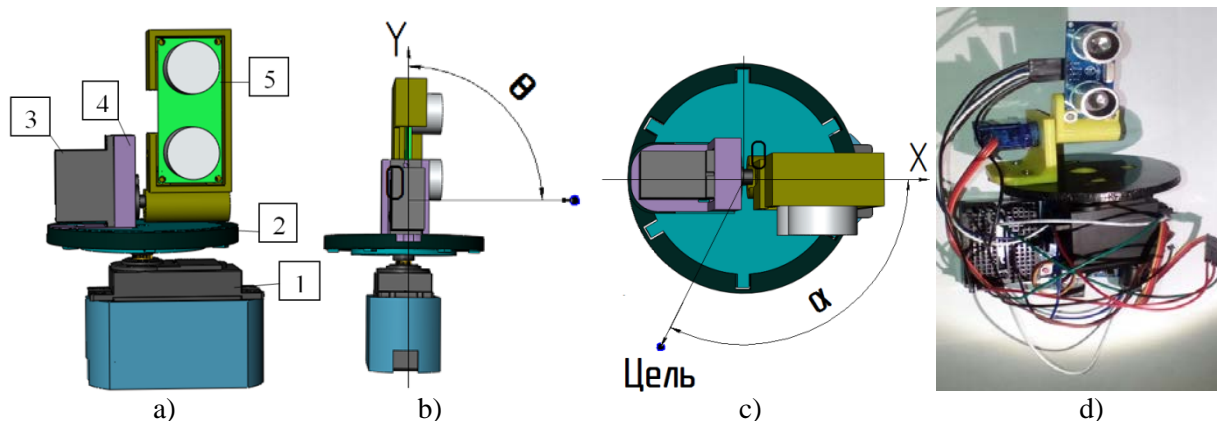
Устройство с УЗ-датчиком: а) вид спереди; б) вид сбоку; в) вид сверху; д) фотография устройства
